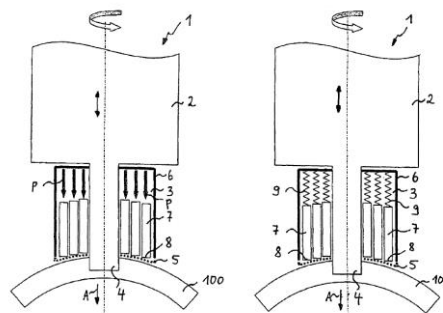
Desenho da ferramenta com a base adaptável.
